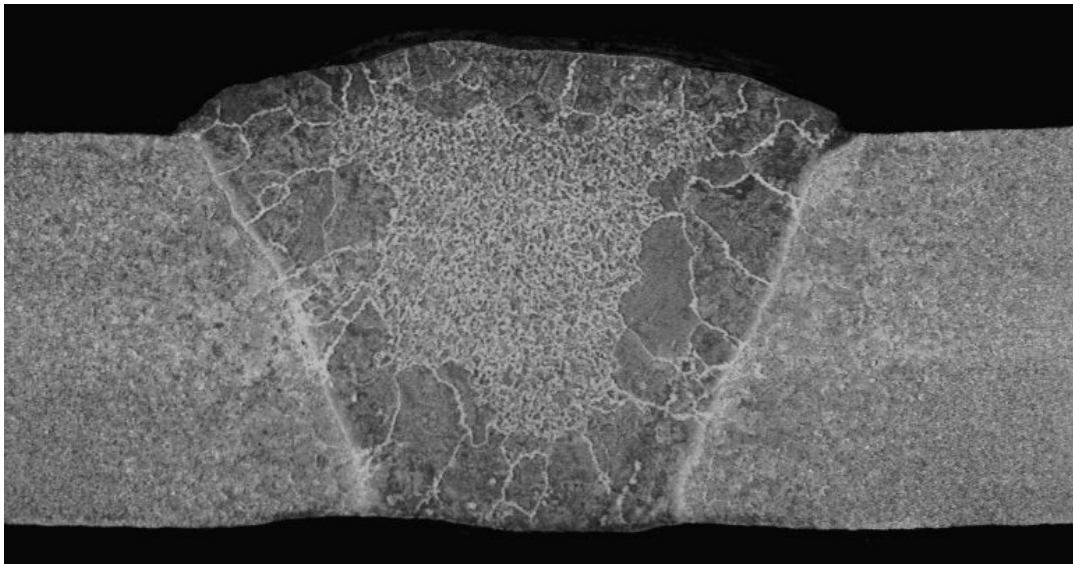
Способ сварки 111. Стыковой шов. (22)
